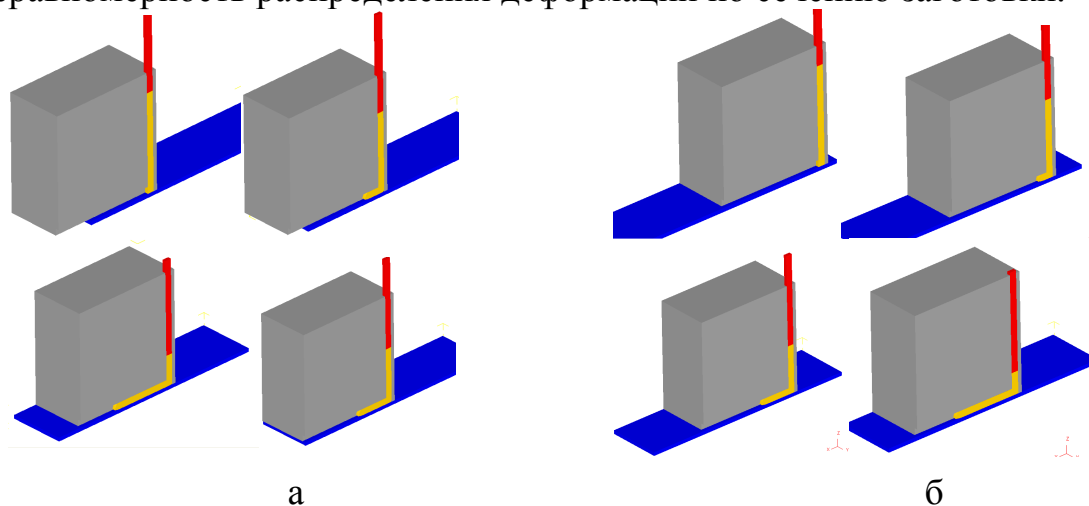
Схемы по стадийного деформирования заготовки РКУП с подвижным дном матрицы (а - движение дна в направлении течения металла заготовки, б - движение дна в направлении противоположном течению металла заготовки)
